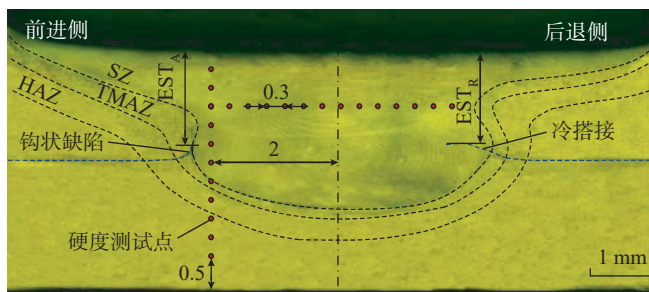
转速1504 r/min、焊速207 mm/min、下压量0.12 mm参数下的接头横截面
